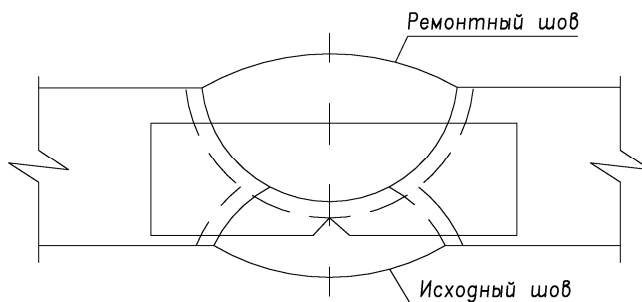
Местоположение надреза ударного образца в сварном шве
